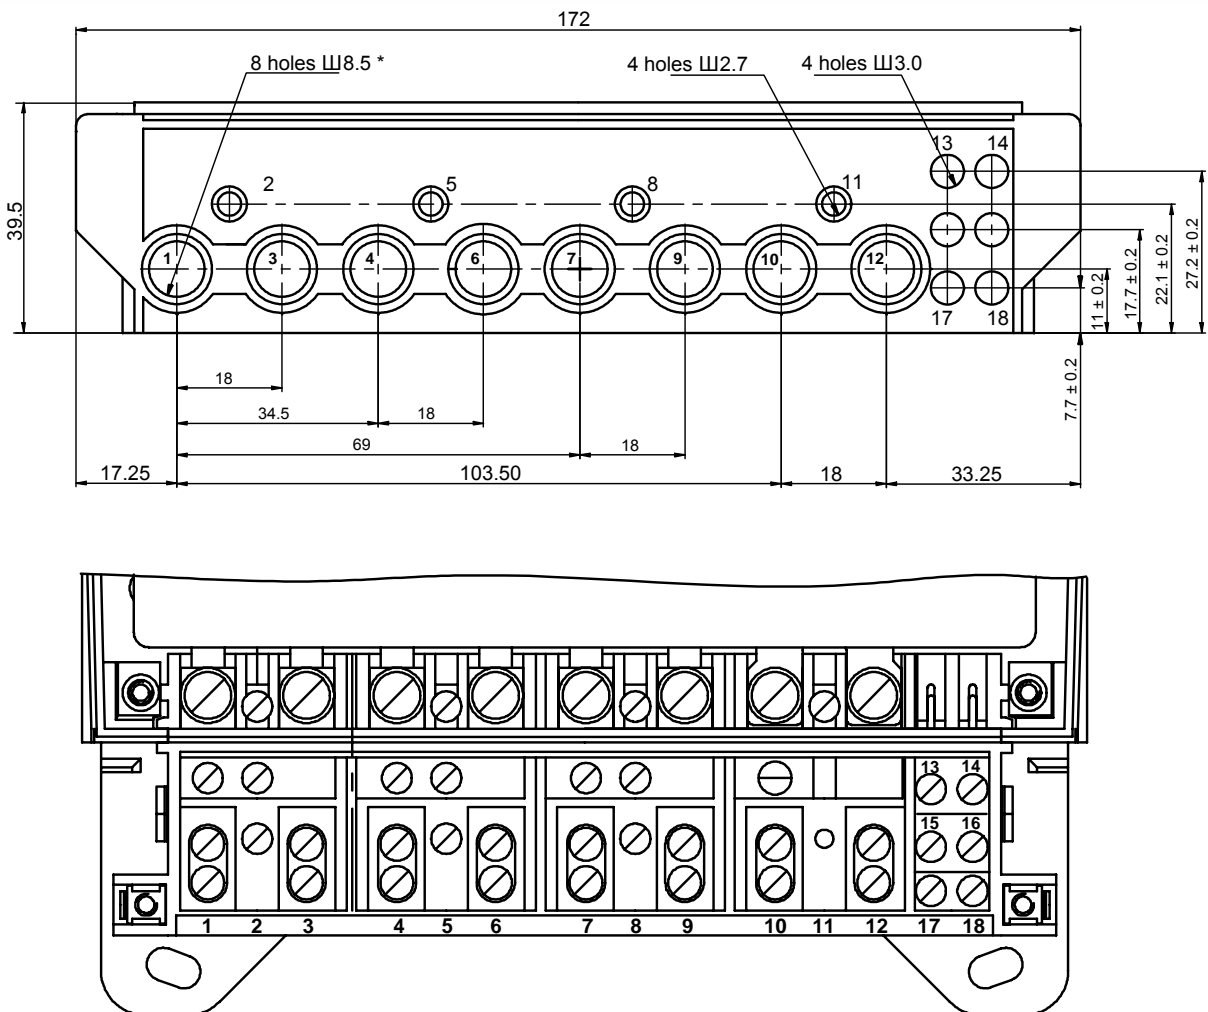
Внешний вид, габаритные размеры и места установки пломб на корпусе типа #3
